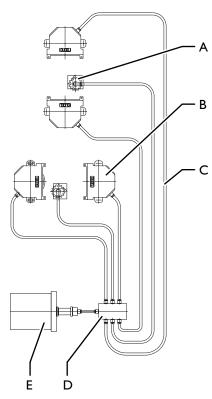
Автоматическая система смазки MEMOLUB - Конструкция
